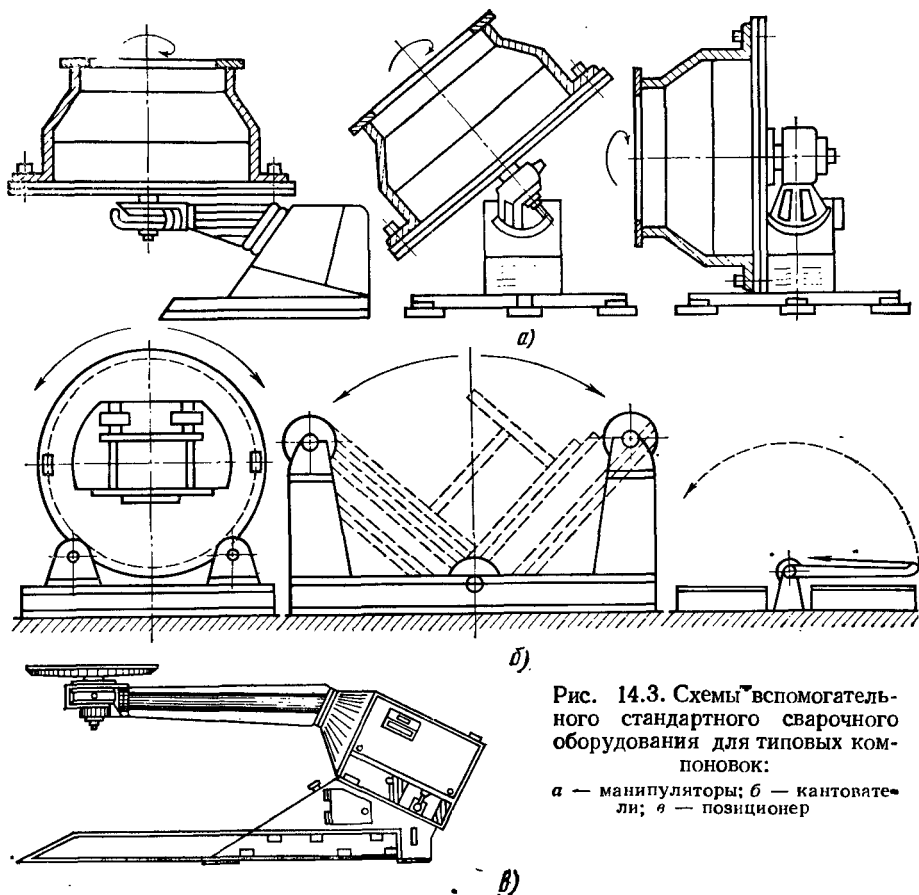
Схемы вспомогательного стандартного сварочного оборудования для типовых компоновок:
